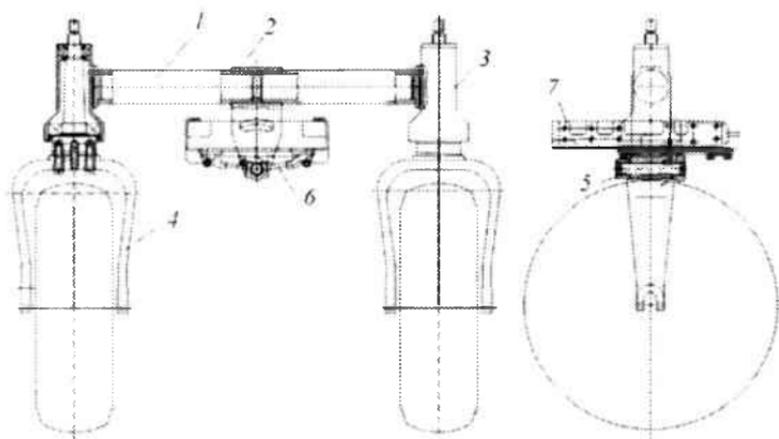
Функциональный передний мост: 1 – полубалка; 2 – корпус; 3 – поворотная цапфа; 4 – вилка; 5 – кронштейн; 6 – передний брус трактора; 7 – ось
